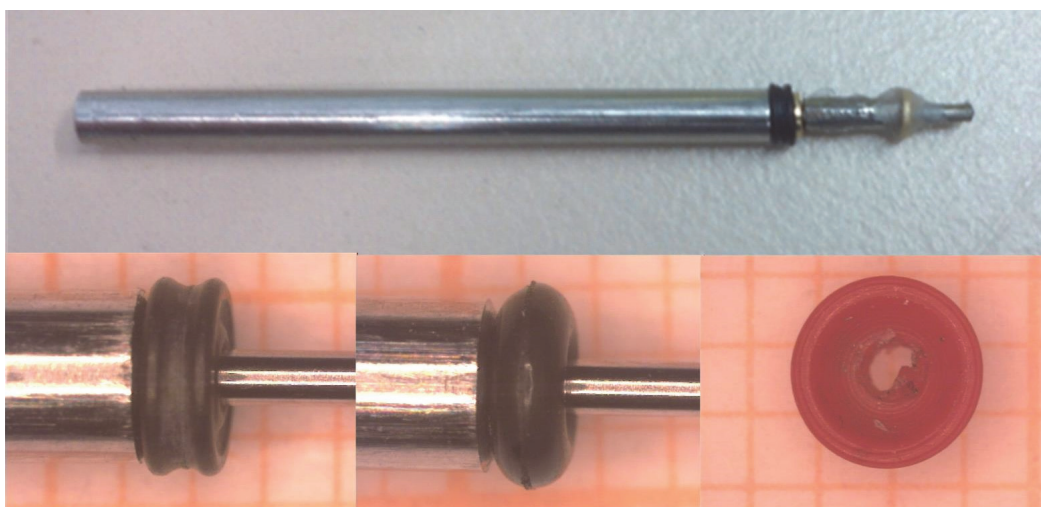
(oben) Testkolben mit schwarzer X-Ring Dichtung, (unten) X-Ring Dichtung (links), O-Ring Dichtung (Mitte), Lippendichtung (links) mit Millimeterpapier im Hintergrund
